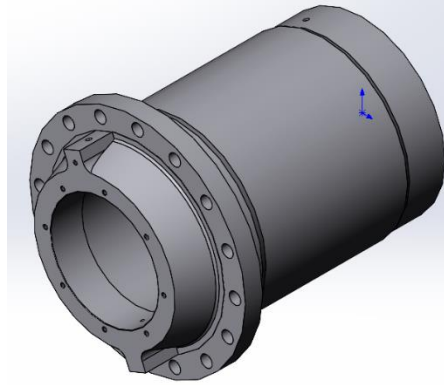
3Д-модель деталі “Корпус”
